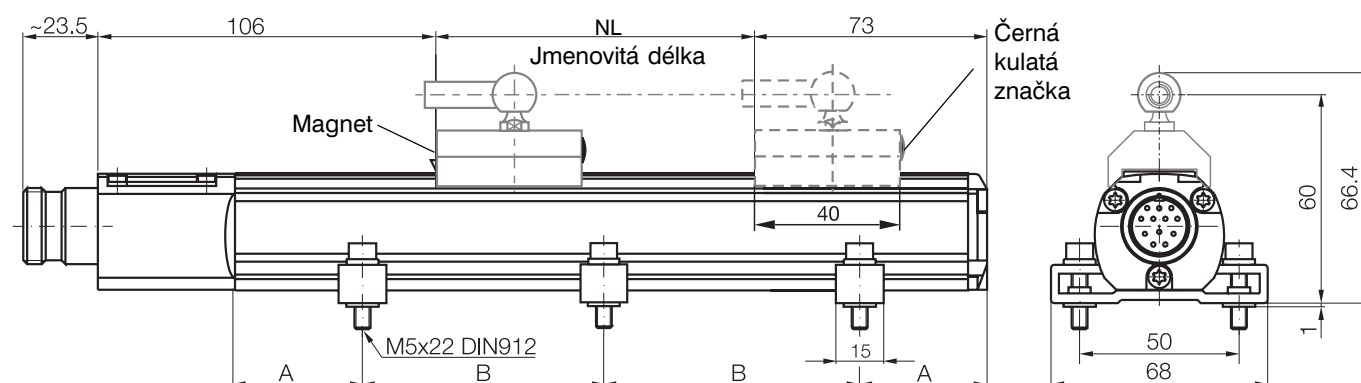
Rozměrový výkres (BTL5...P-S 86 odměřování s volným magnetem BTL5-P-3800-2)
